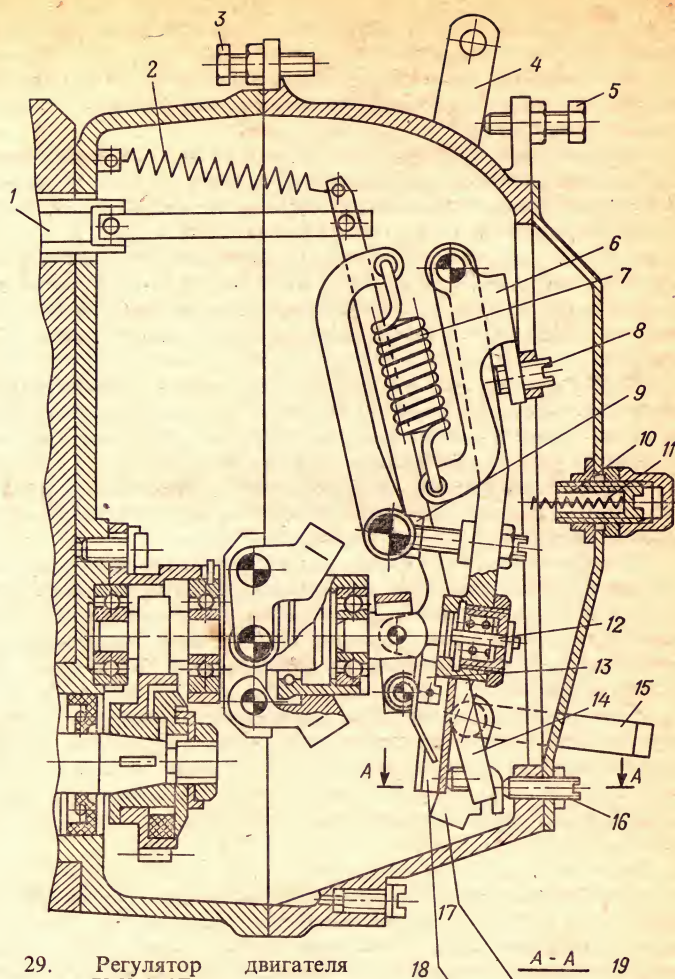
Регулятор двигателя ЯМЗ-240Б:
